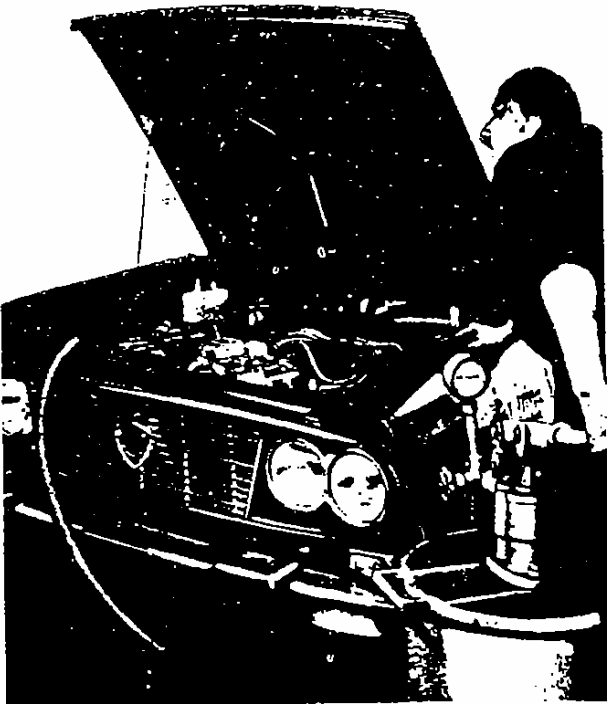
/19 - Essai sous pression de l'étanchéité hydraulique de la culasse et du bloc-cylindres.
